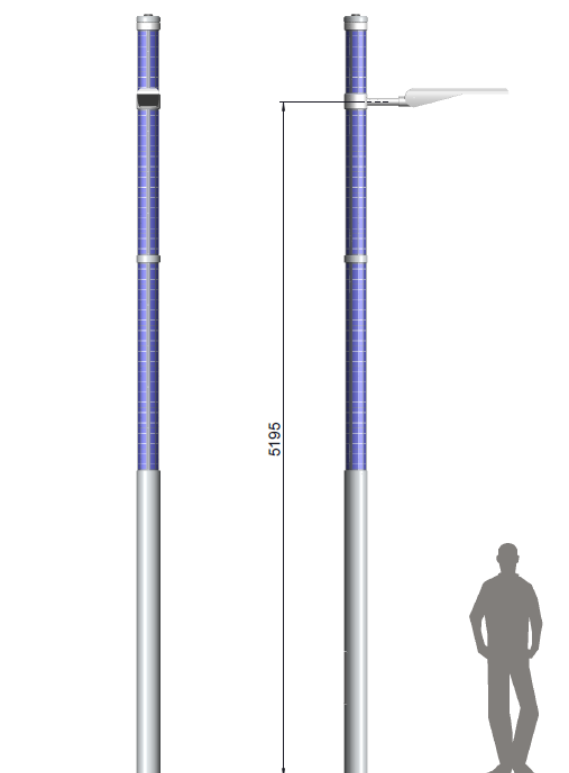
Габаритные размеры установки ОСО-40-12-125-100
